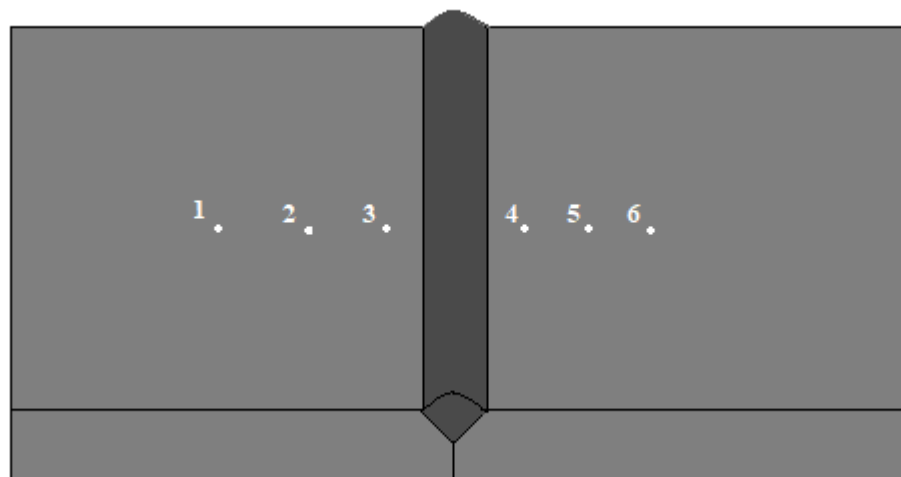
Pontos de medição de dureza das peças soldadas.
